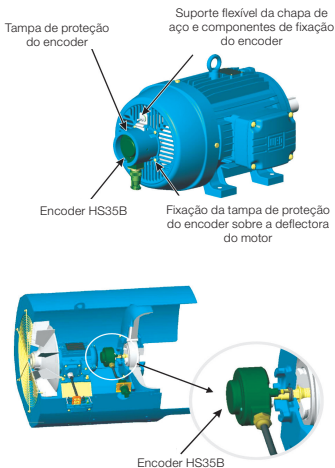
Montagem do Encoder HS35B para o motor auto-ventilado, ou com ventilação forçada
